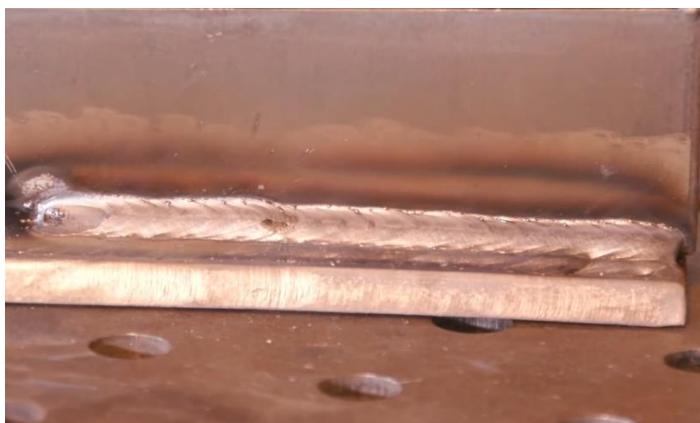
Загальний вигляд кутового зварного шва таврового з'єднання
